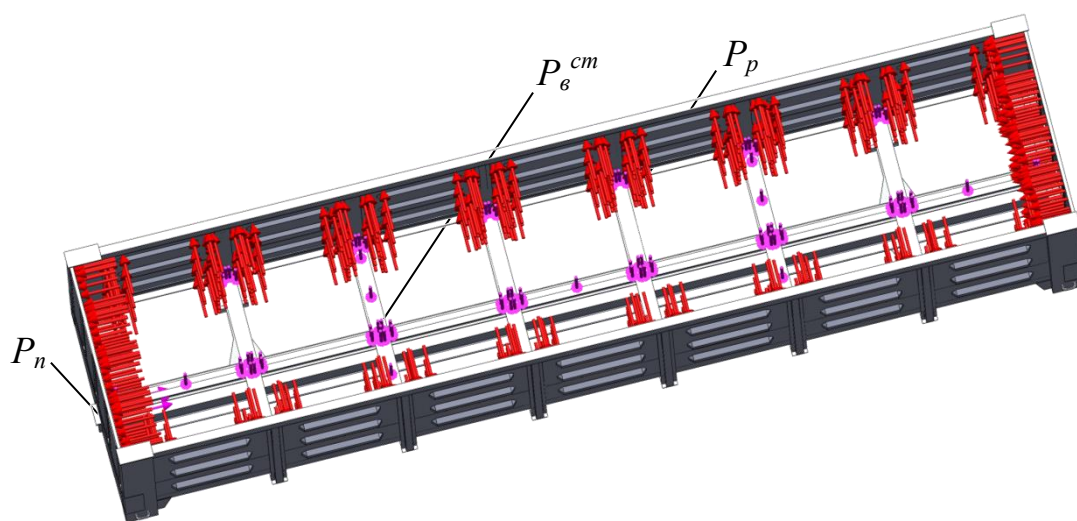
Розрахункова схема несучої конструкції напіввагона
